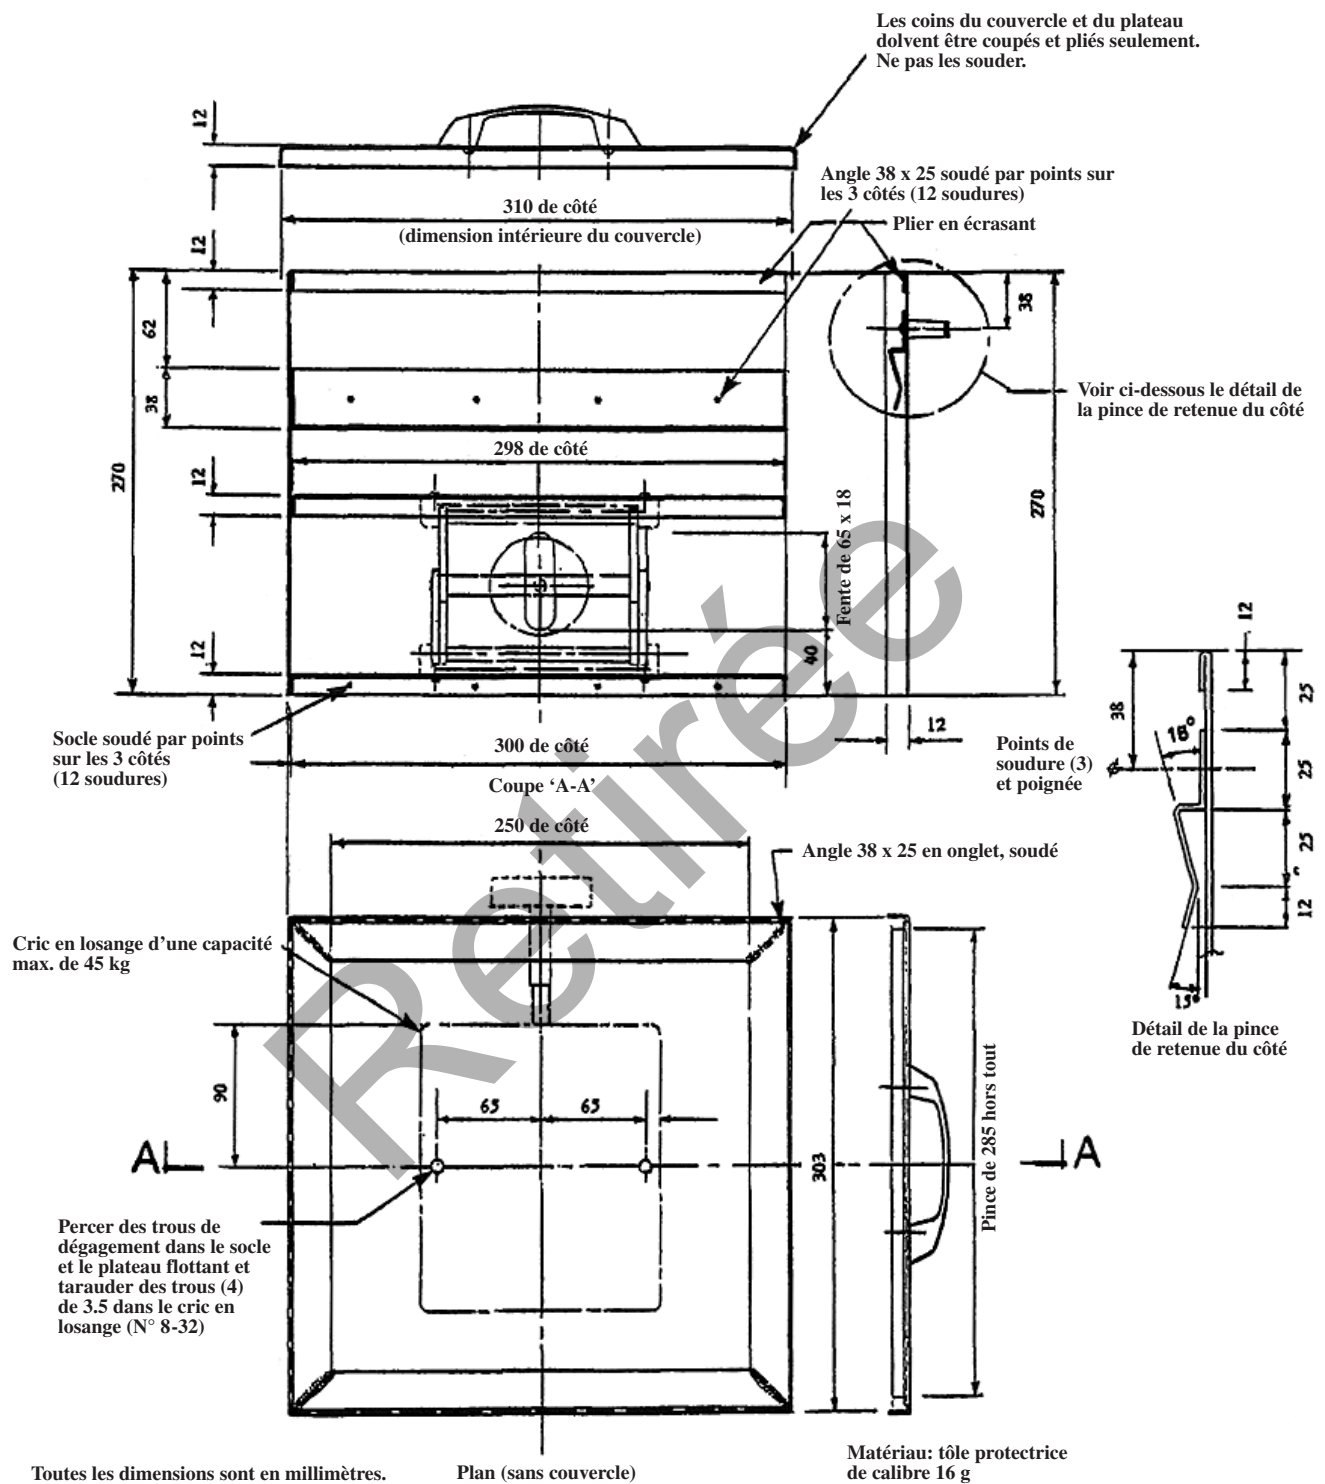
Plan d'ensemble du caisson d'essai d'inflammation des matelas
